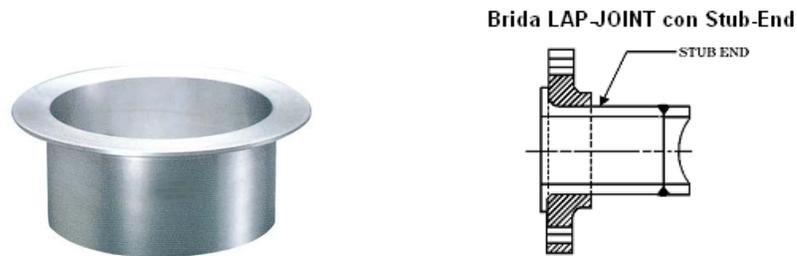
Stub end y Brida loca (Lap Joint)
